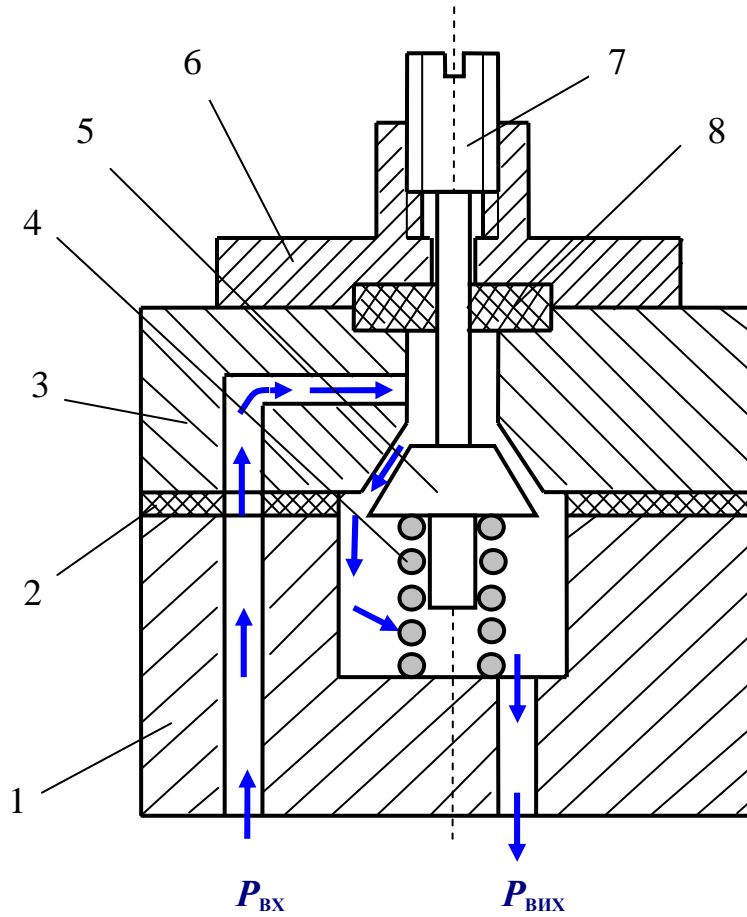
Змінний пневматичний опір П2Д.2М: 1 – нижня частина корпусу; 2 – гумова прокладка; 3 – верхня частина корпусу; 4 – пружина; 5 – зворотний клапан з голковим штирем; 6 – фланець притискання; 7 – гвинт, який регулює зазор провідності дроселя; 8 – ущільнююче гумове кільце
